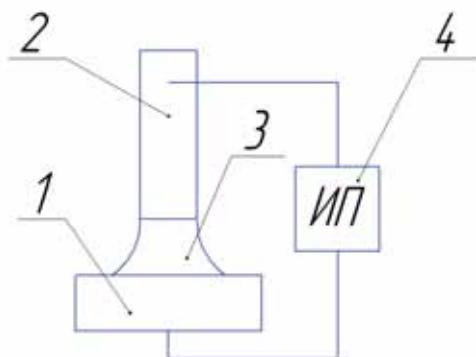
Электрическая сварочная цепь дуговой сварки:
